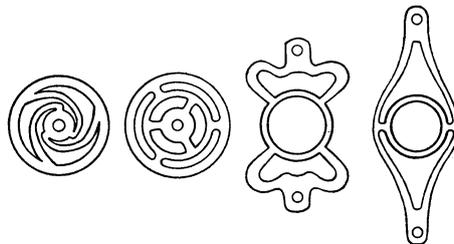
Ältere Formen von Zentrierspinnen für dynamische Lautsprecher; links zwei für Befestigung innen; rechts zwei für Befestigung außen
